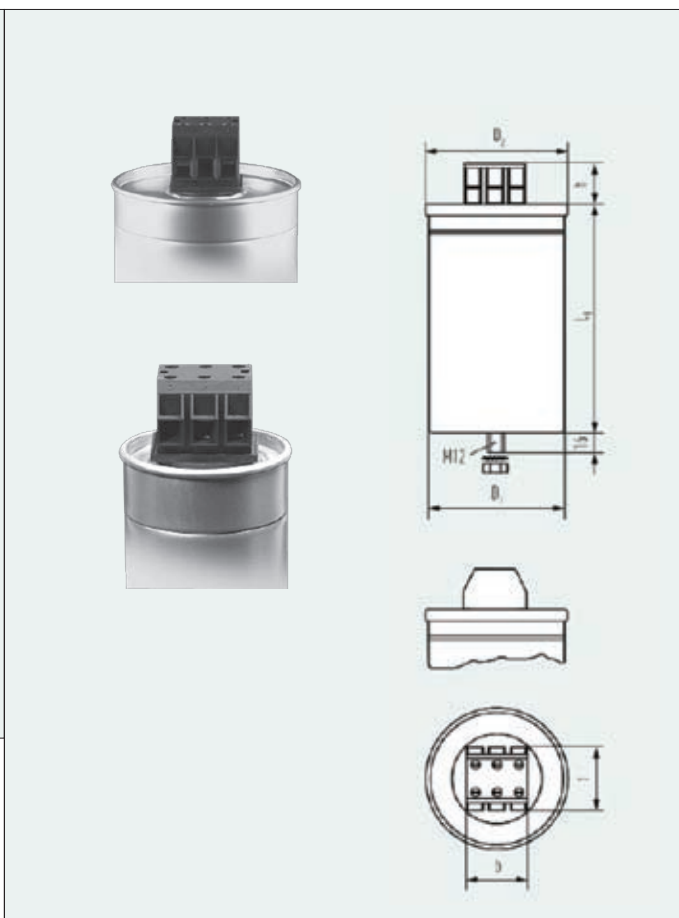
Конструктивное исполнение конденсатора E62.XXX/276.XXX
